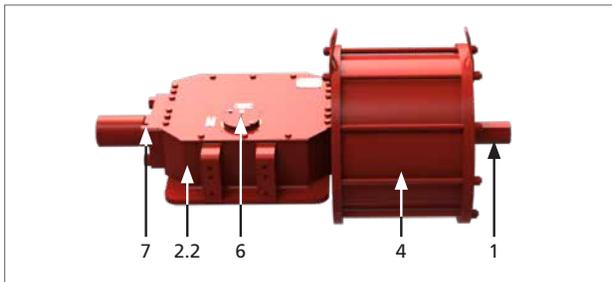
Componentes principais do GPID (corpo soldado)
